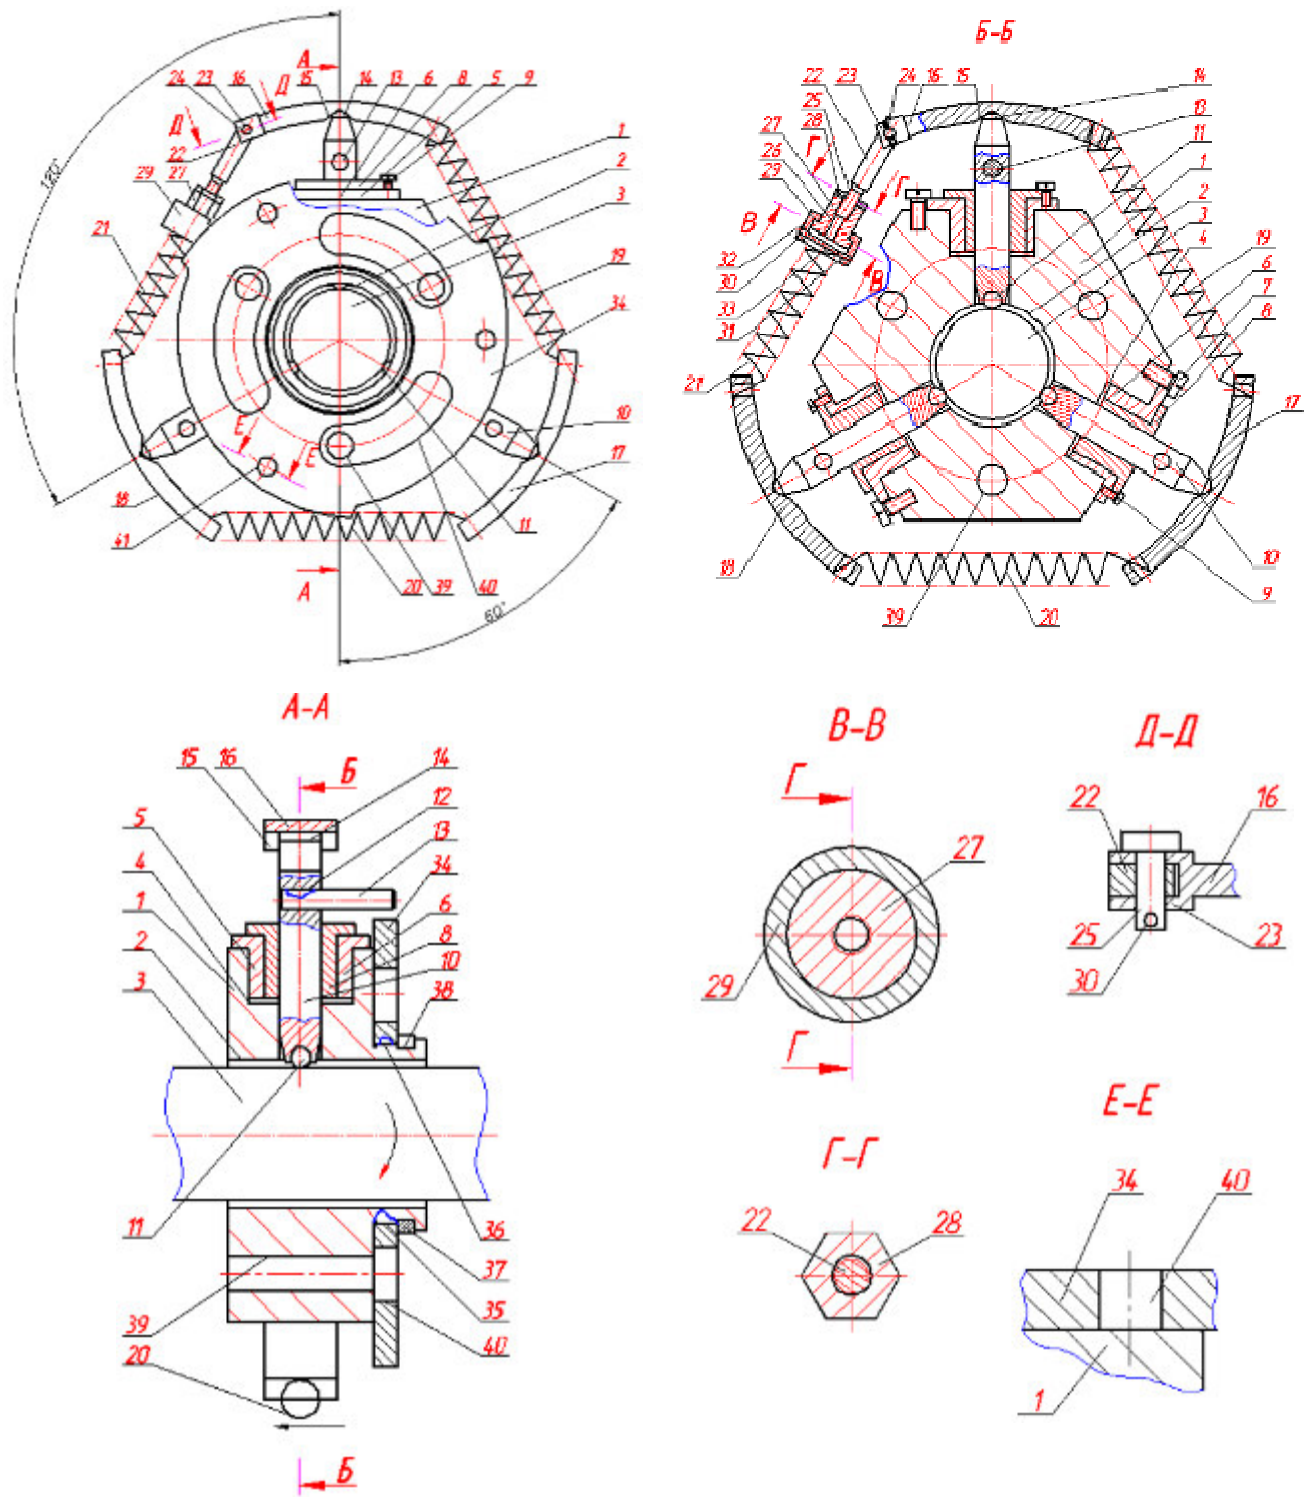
Ескіз інструменту для формування регулярних мікрорельєфів на зовнішніх циліндричних поверхнях [233]
